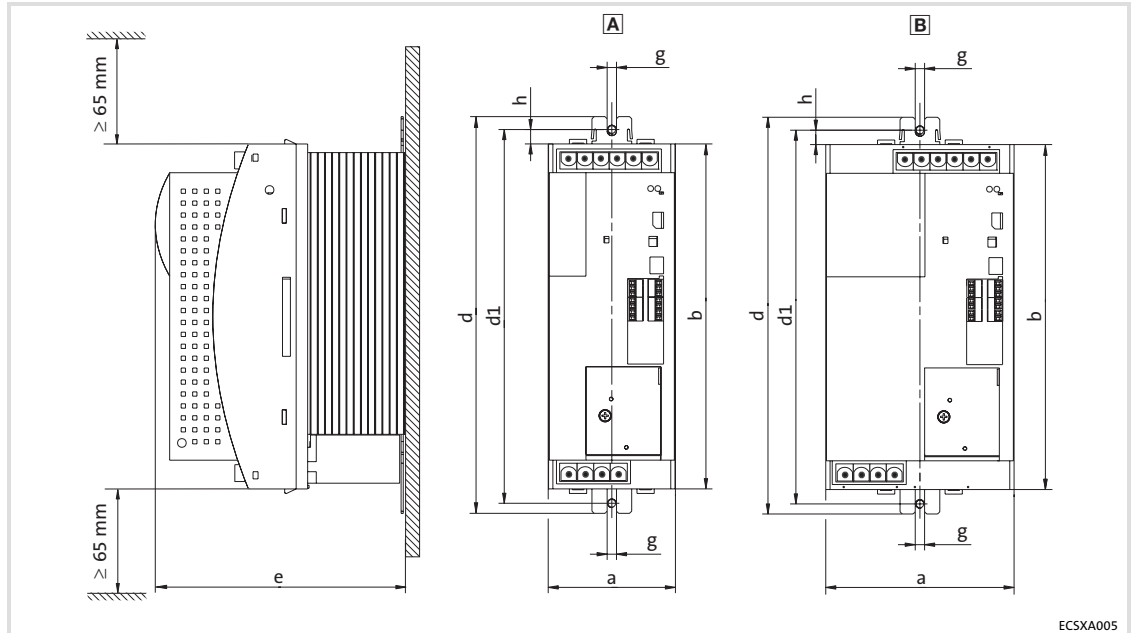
Dimensioni per il montaggio standard con guide di fissaggio
